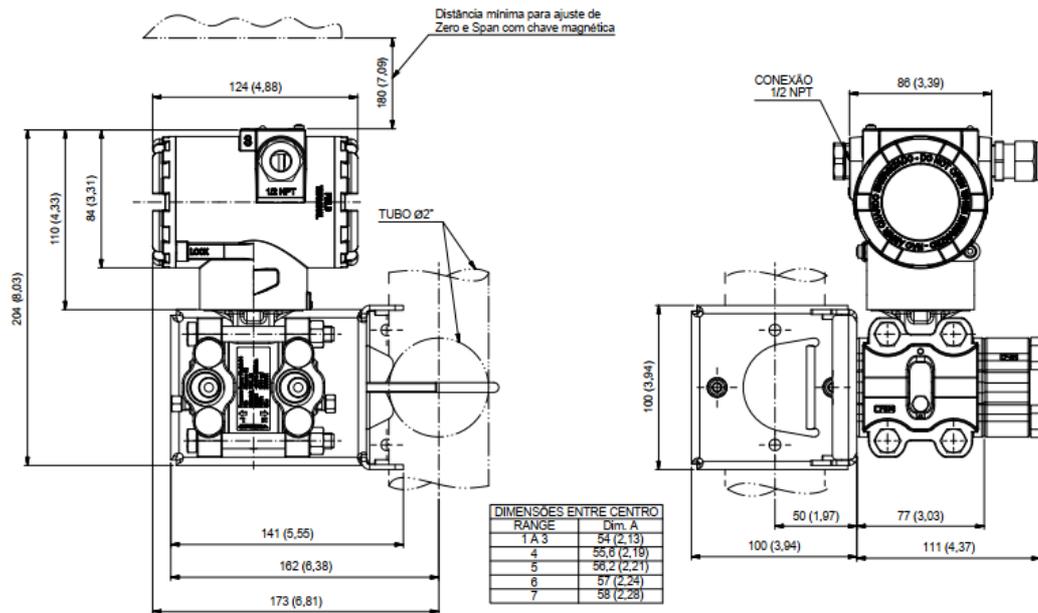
Desenho dimensional e esquema de montagem do VPT10 HART com sensor remoto.
